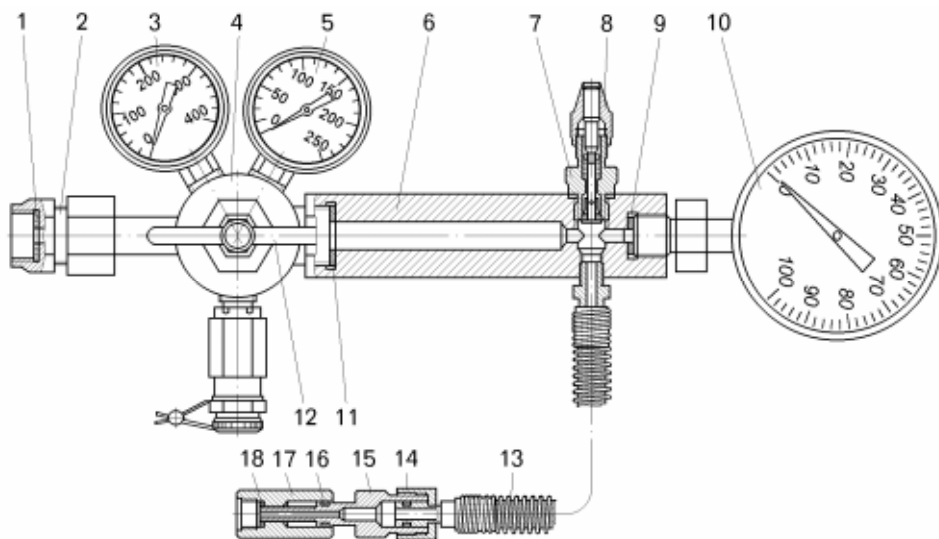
Приспособление для зарядки цилиндров подвески:
